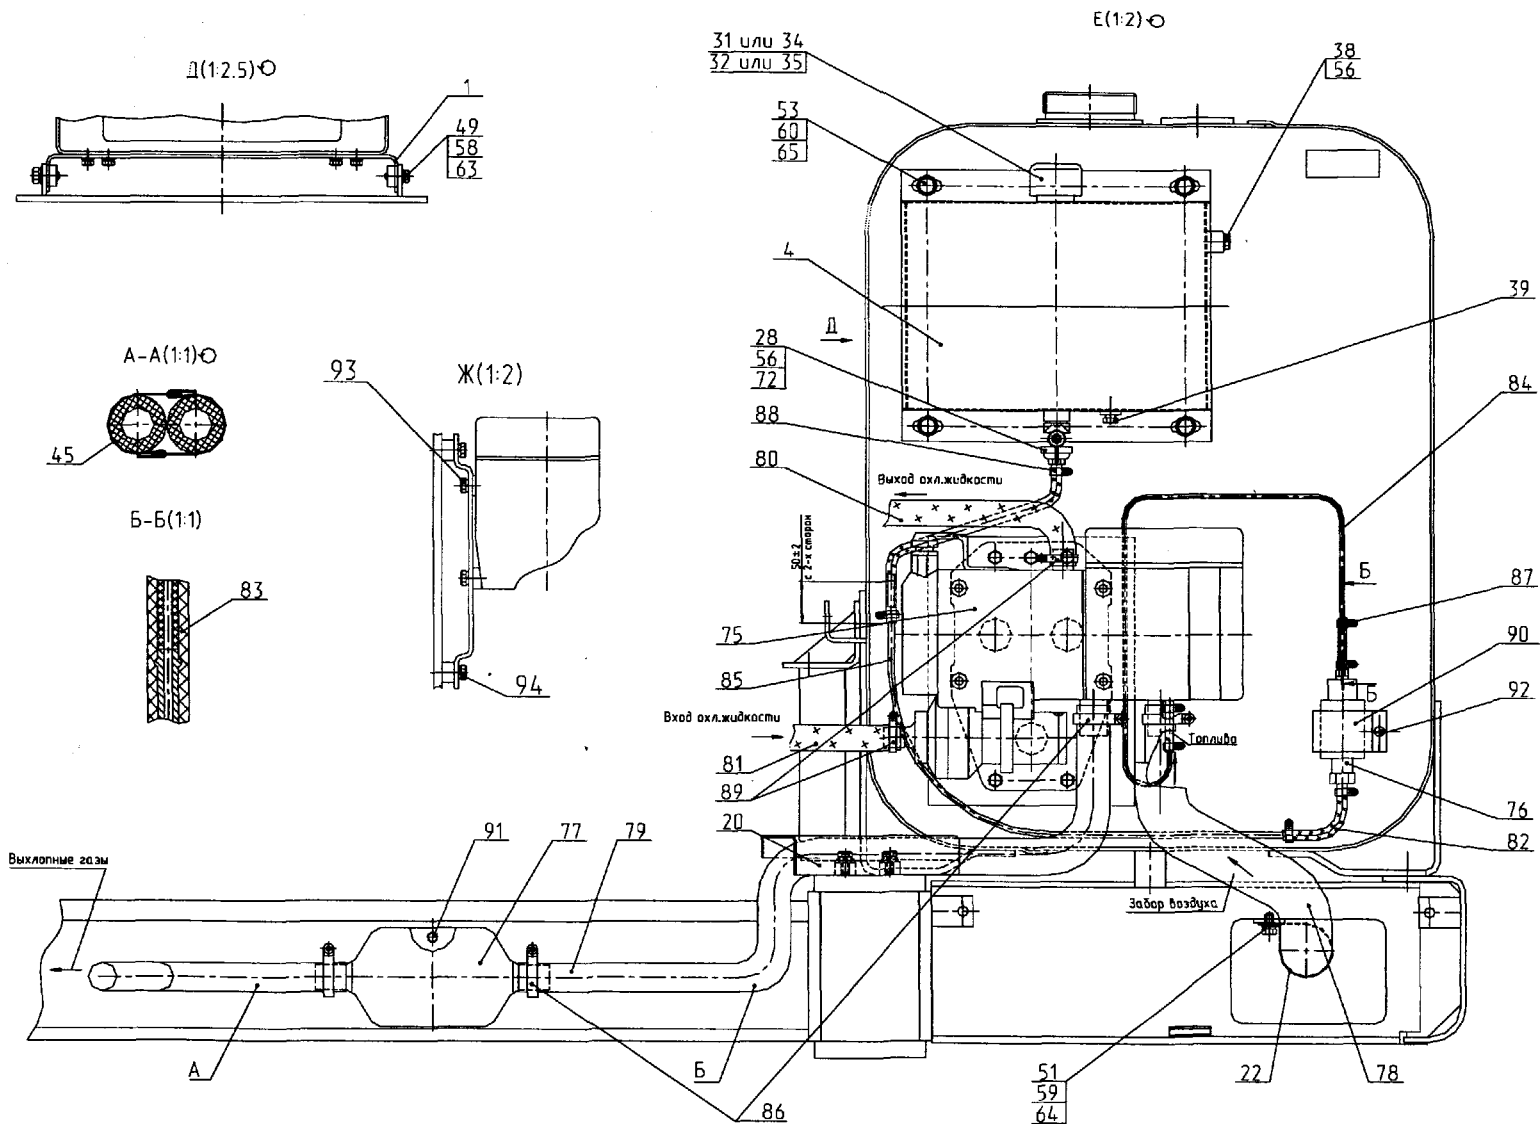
Установка предпускового подогрева двигателя и отопления кабины:
